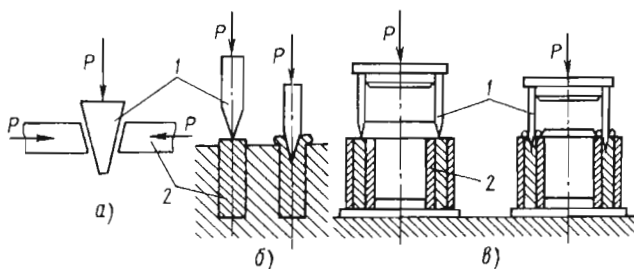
Технологические схемы клинопрессовой сварки:
